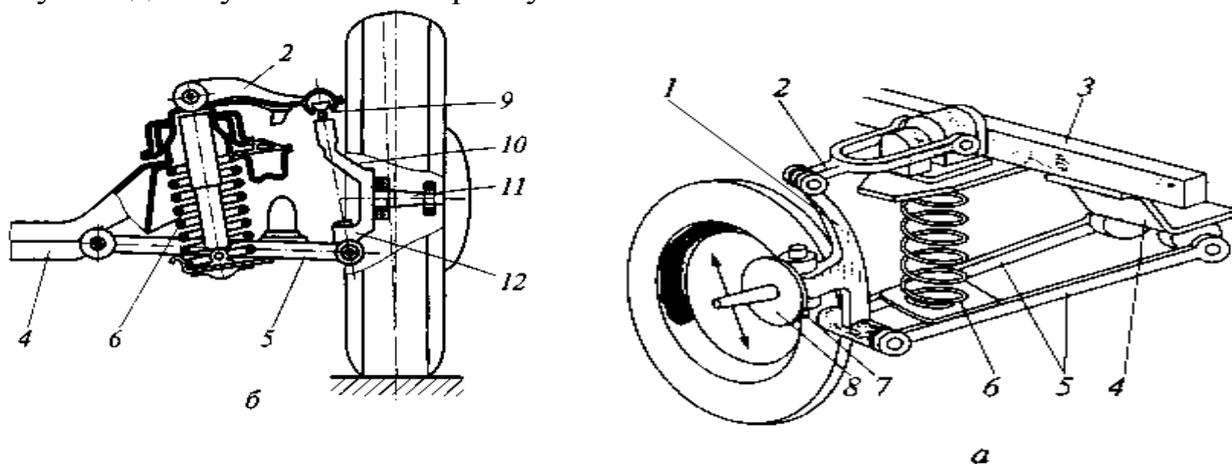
Схема независимой подвески колес: а — шкворневая подвеска; б — бесшкворневая подвеска; 1, 10 — стойки; 2 — верхний рычаг; 3 — подрамник; 4 — балка передней оси; 5 — нижние рычаги; 6 — пружинная рессора; 7 — шкворень; 8 — поворотная цапфа; 9, 12 — шаровые поверхности; 11 — поворотный кулак
